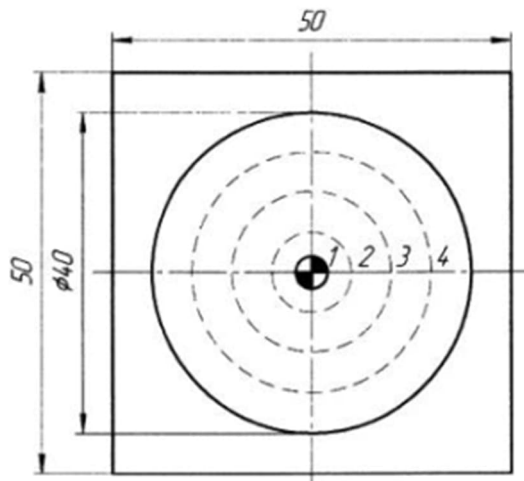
Чорнове фрезерування круглого кармана
